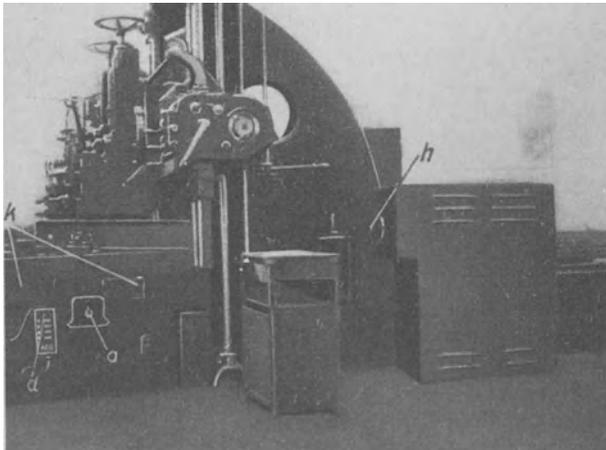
Elektrische Umsteuerung der Hobelmaschinen.
